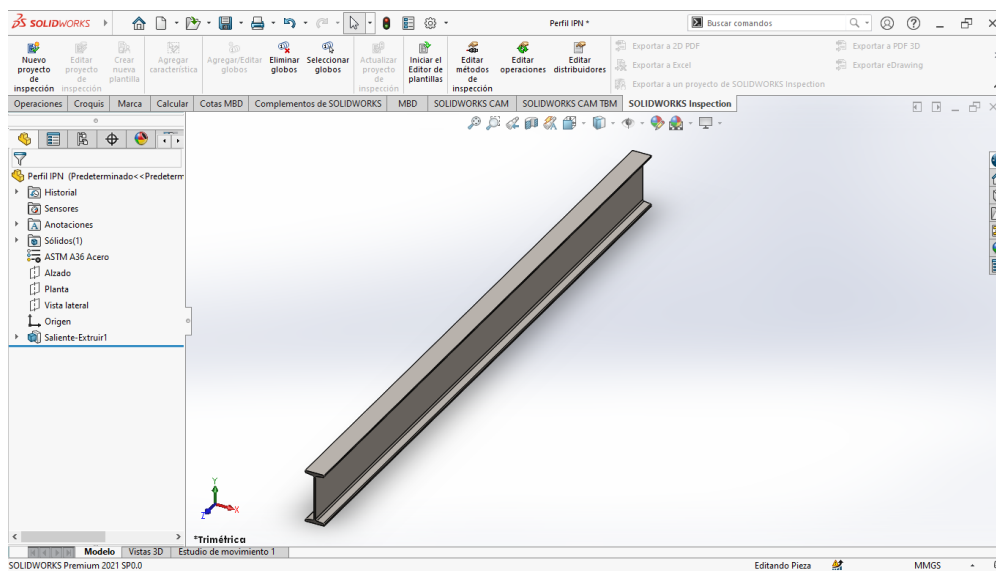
Viga principal perfil IPN 220, material acero A-36. Fuente: Autor
